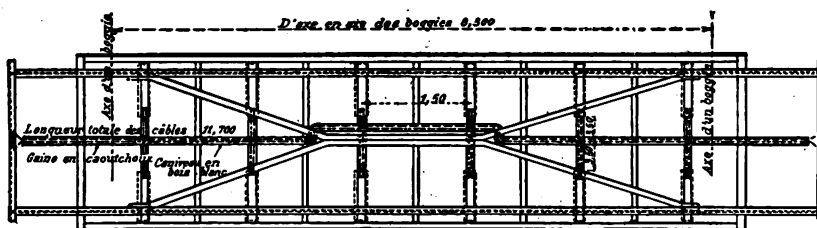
Emplacement des chaufferettes dans une voiture. (Vue par dessous.)
